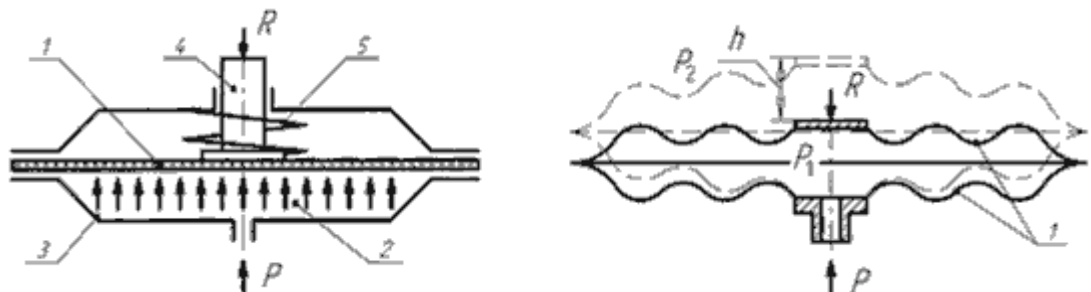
Схемы мембран: а - плоская с эластичным кольцом; б - гофрированная металлическая.
